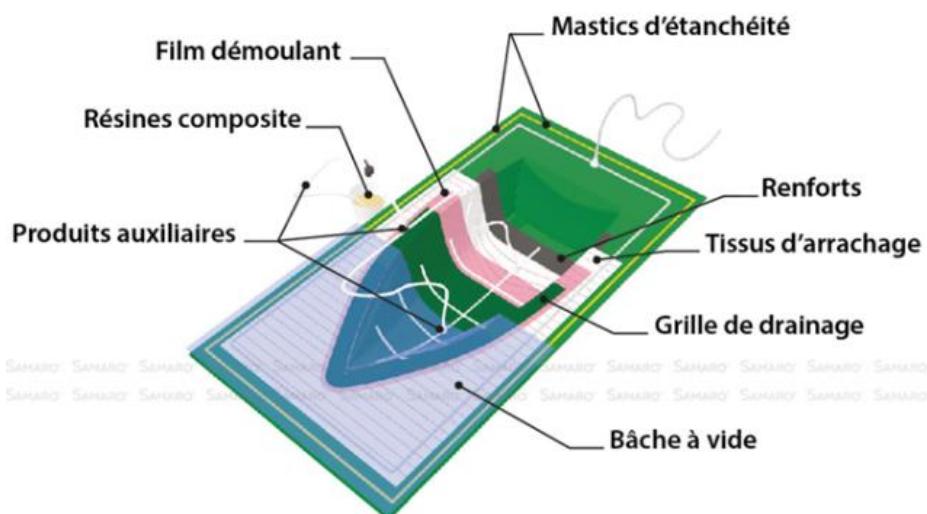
Le procédé d'infusion pour un moule de coque de bateau [16]
